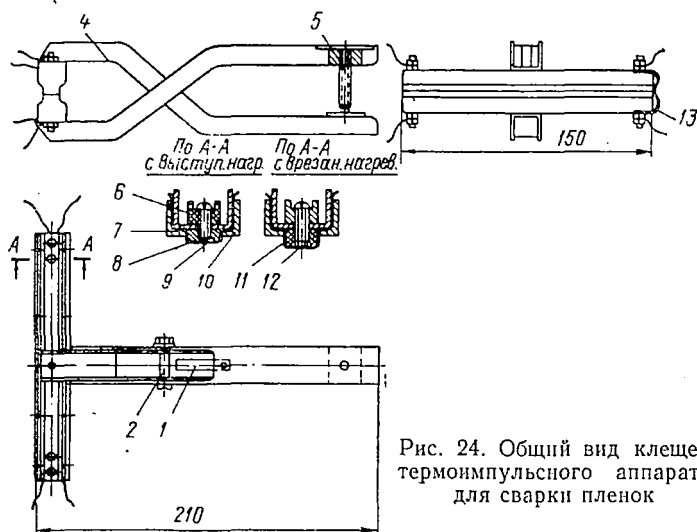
Общий вид клещей термоимпульсного аппарата для сварки пленок
